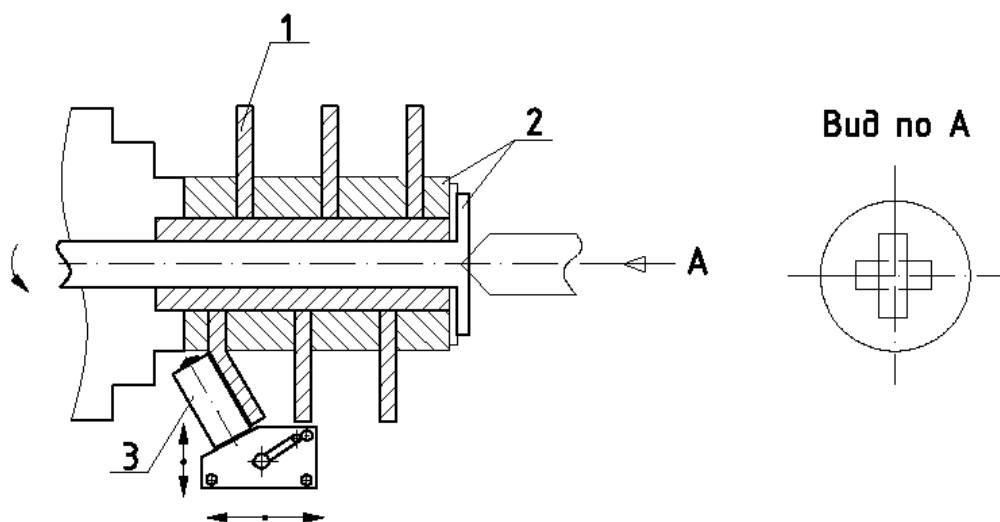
Конструктивна схема пристрою для виготовлення вигнутого профілю на гвинтових заготовках: 1 – ГЗ; 2 - система кріплення ГЗ; 3 - формувальний інструмент
